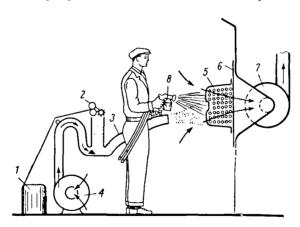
Схема установки для предварительного формования шланговым способом:
